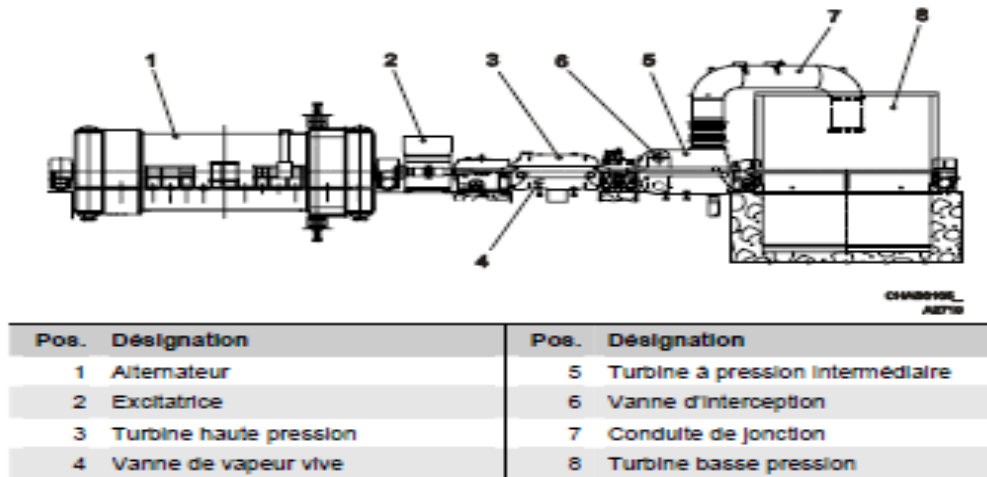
Dessin d'ensemble de la turbine à vapeur
